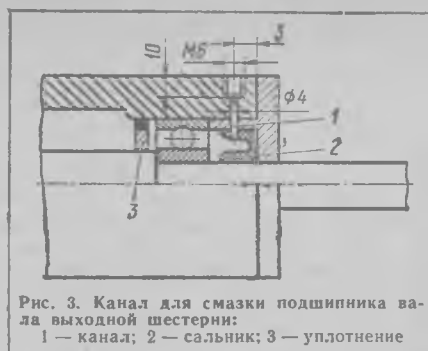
Канал для смазки подшипника вала выходной шестерни: 1 — канал; 2 — сальник; 3 — уплотнение
